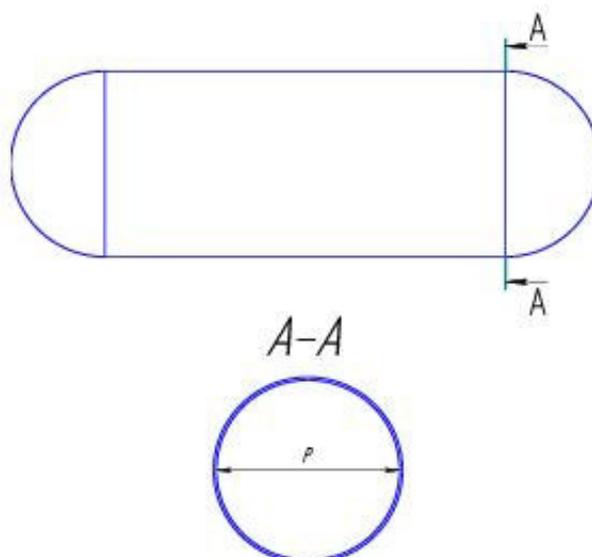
Изображение сварного шва на ресивере и действие давления P на сварной шов
